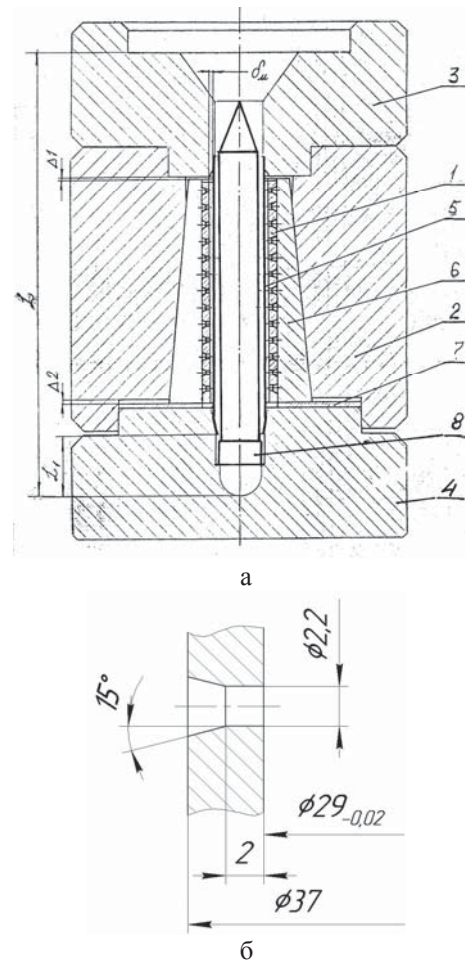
Конструктивная схема оснастки с профилированными отверстиями матрицы и разрезной обоймой (а):
